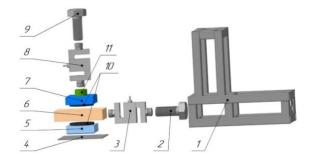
Установка для определения коэффициента трения: 1 — корпус; 2, 9 — винт M 24 х50; 3 — тензодатчик динамометра № 1; 4 — крышка; 5, 7 — контактный элемент; 6 — образец древесины; 8 — тензодатчик динамометра № 2; 10 — вкладыш из упругоподатливого материала; 11 — толкатель
